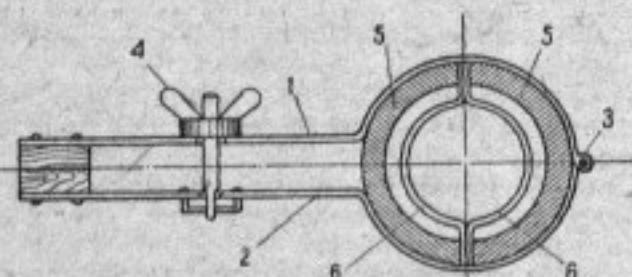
Приспособление для заливки крышек шатунных и коренных подшипников
